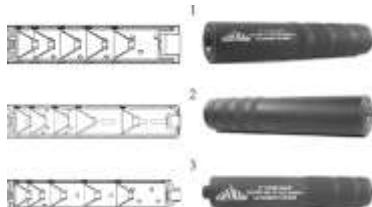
Конструктивная схема и внешний вид приборов снижения уровня звука выстрела:
